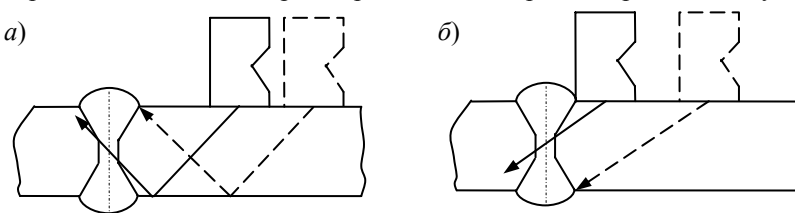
Схемы контроля стыковых сварных соединений:
